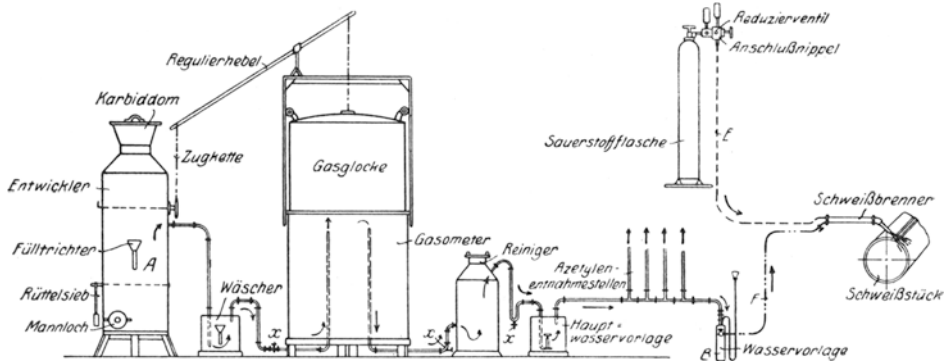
Schema einer ortsfesten Azetylen-Schweißanlage.
